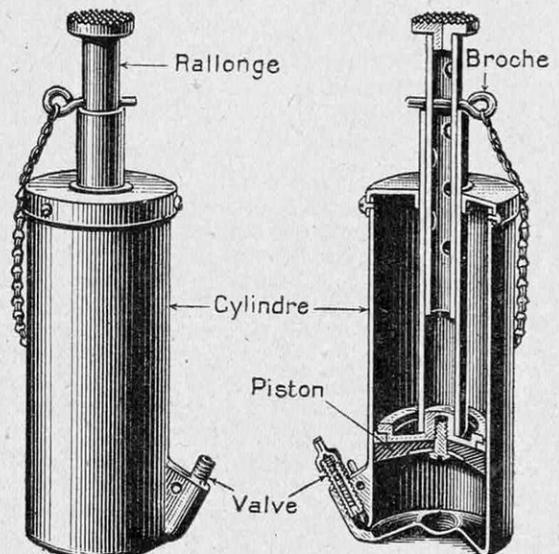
VUE ET COUPE DU NOUVEAU CRIC PNEUMATIQUE
